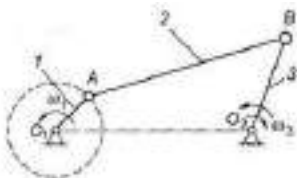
Шарнирный четырехзвенный механизм: 1 — кривошип; 2 — шатун; 3 — коромысло
